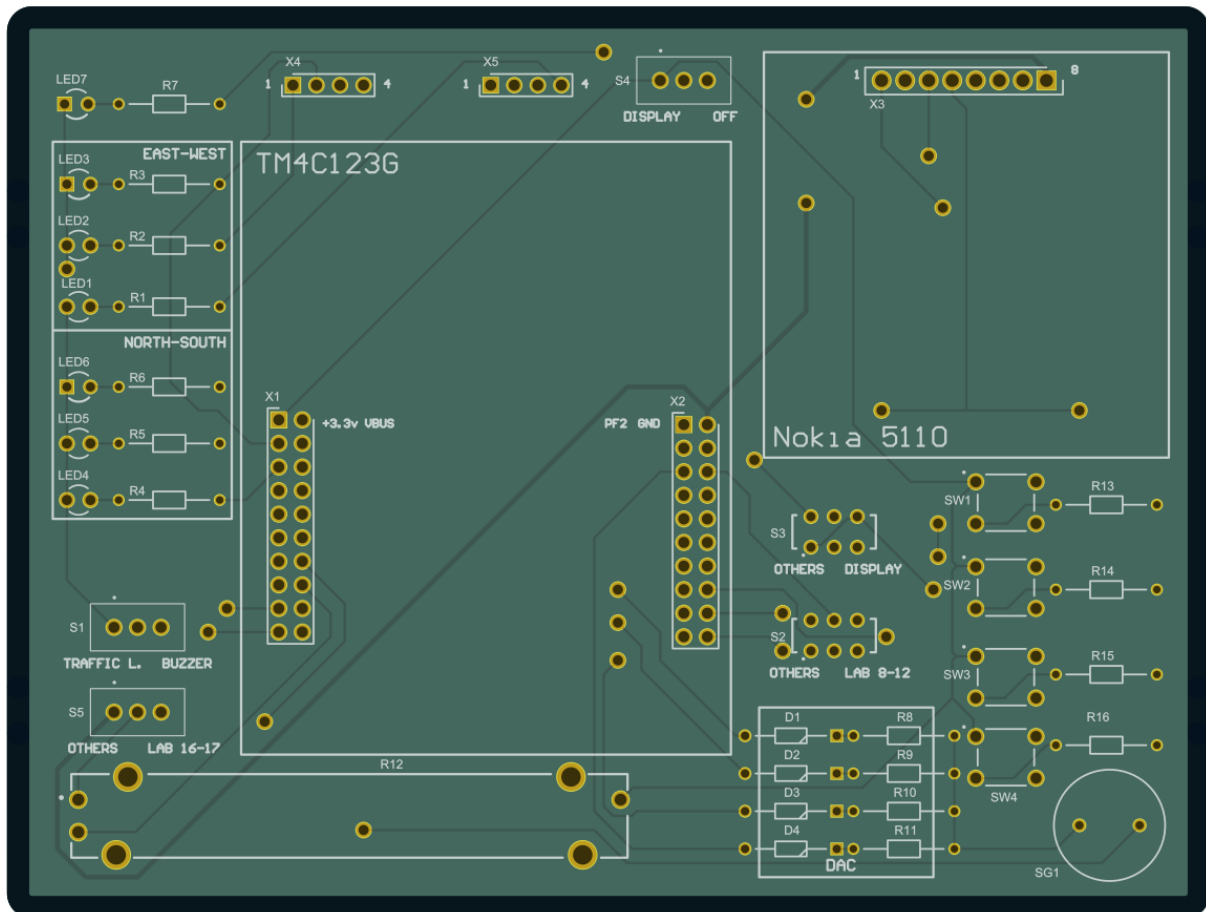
Confirmació del disseny de la PCB a fabricar, cara superior.
